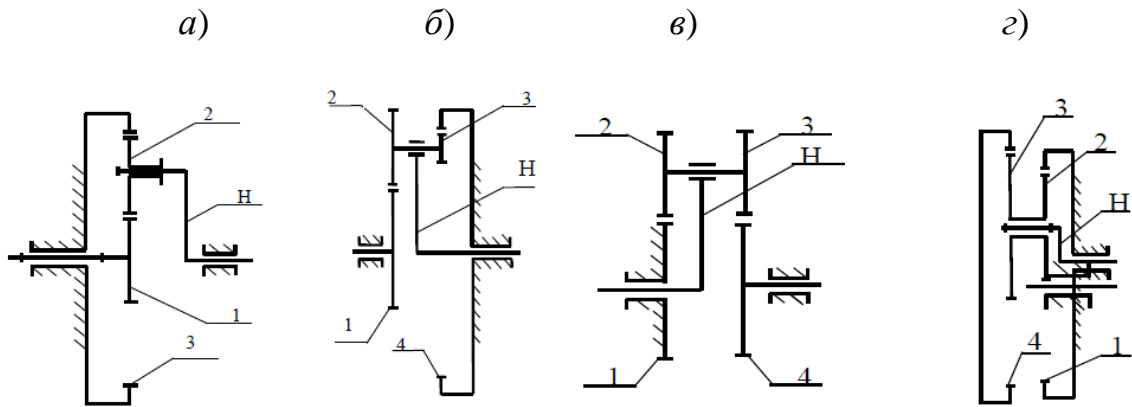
Схемы планетарных зубчатых механизмов: а) механизм Джеймса; б) механизм со сдвоенными сателлитами; в) механизм Давида; г) механизм со сдвоенными сателлитами и двумя внутренними зацеплениями
